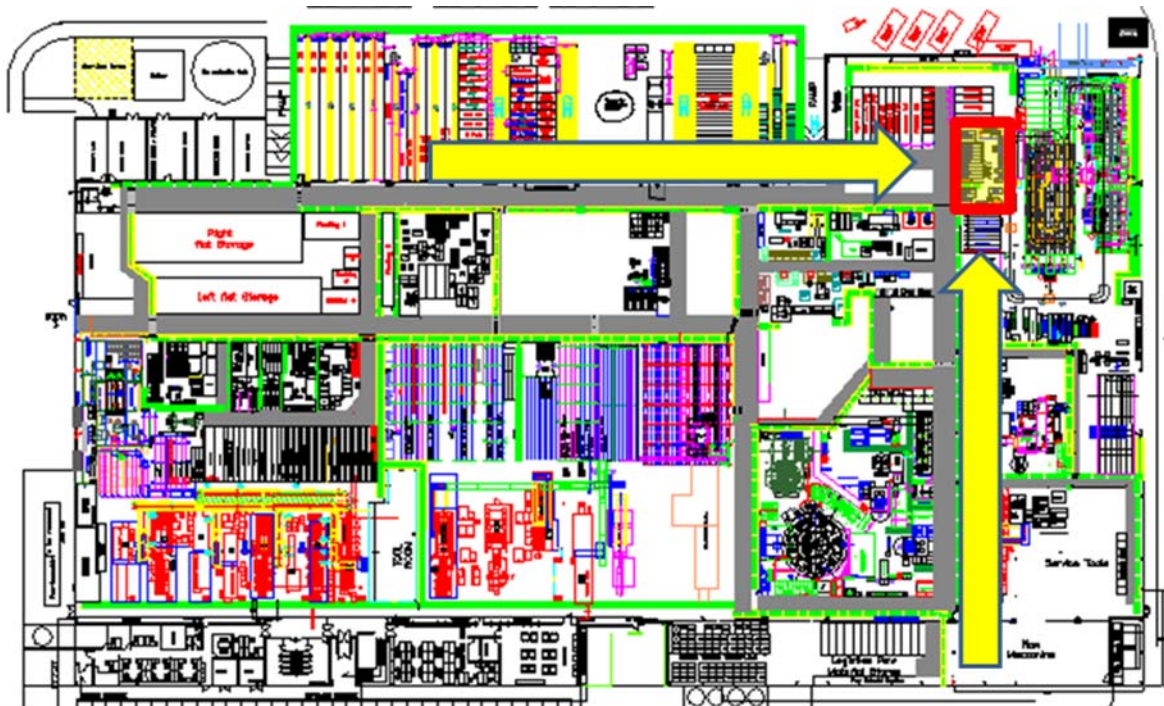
Master Layout señalando la zona aplicada
